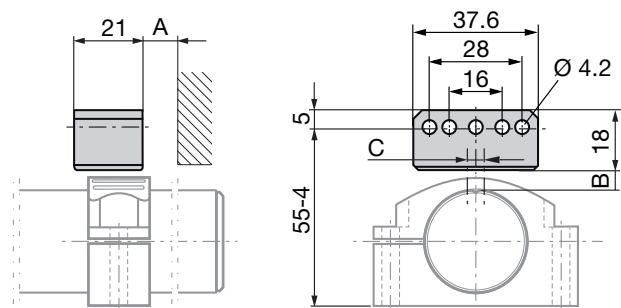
Dimensions et distances pour le capteur de position BTL6-A-3801-2
